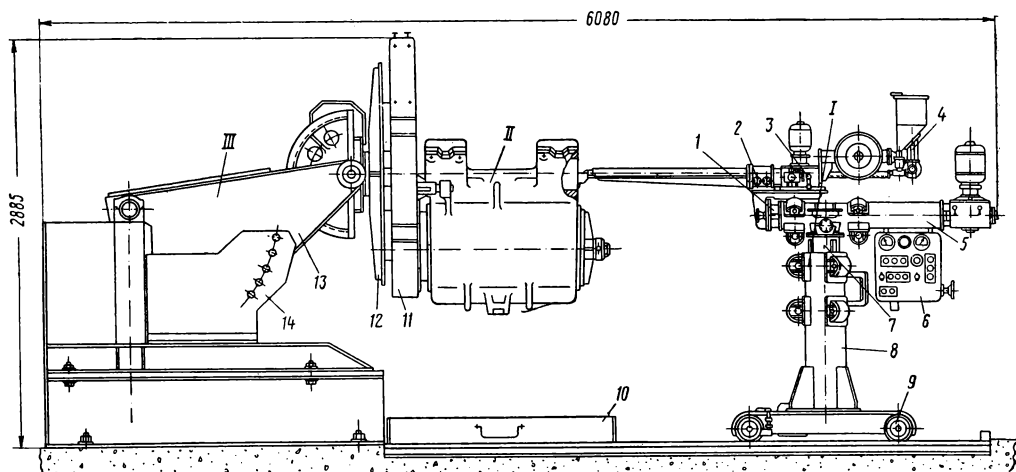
Установка для наплавки под слоем флюса остовов тяговых двигателей:
